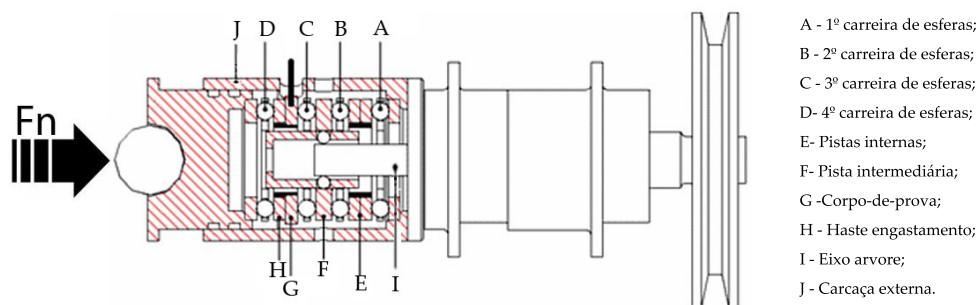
Vista em corte da câmara de ensaio (adaptado de Brunetti, 2008).
